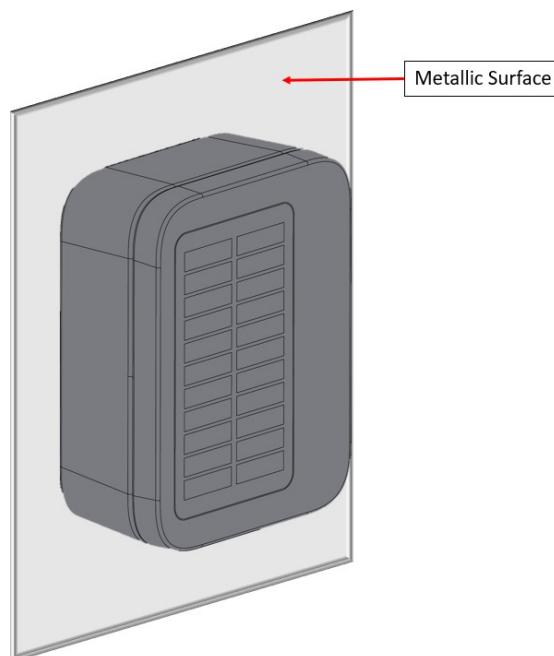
Befestigung des Gehäuses an der Metallocberfläche
